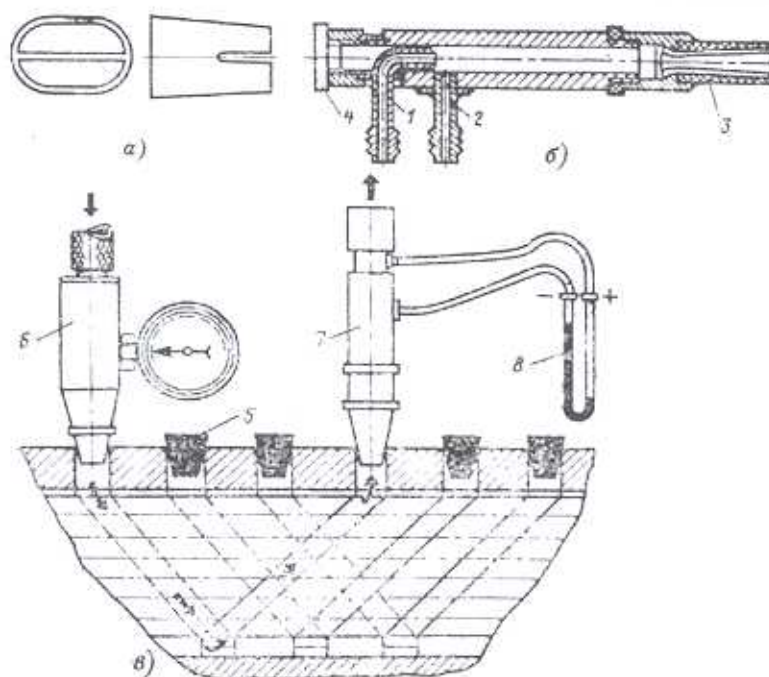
Приспособления для продувки пазовой части обмотки:
